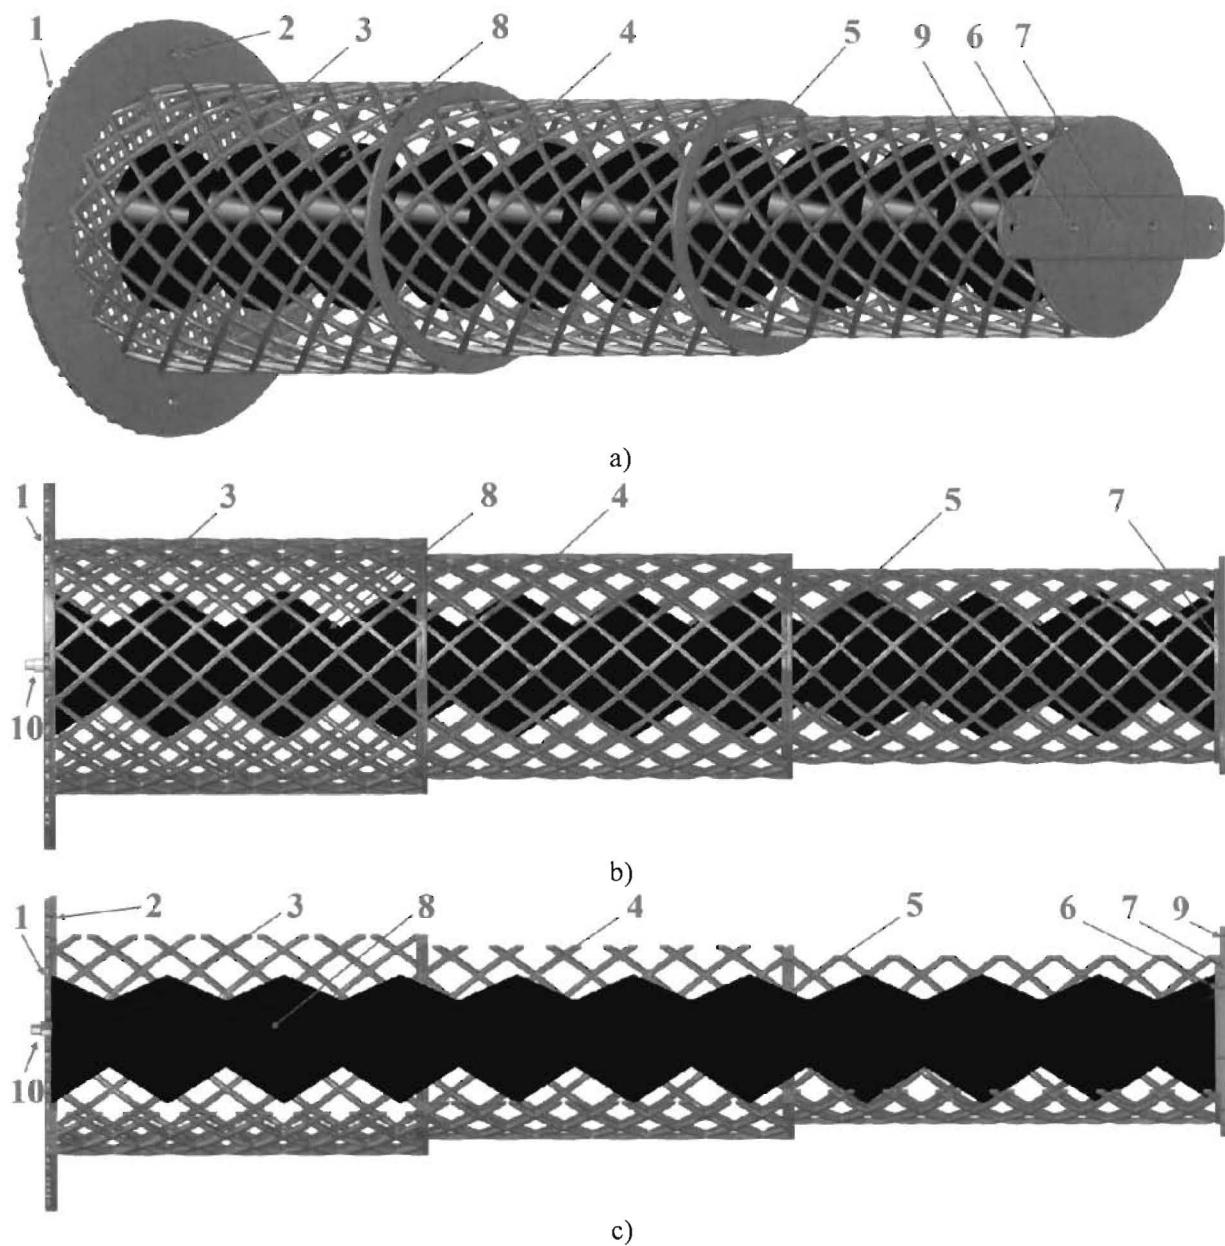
Exemplu de braț telescopic cu structură ușoară și element expandabil
